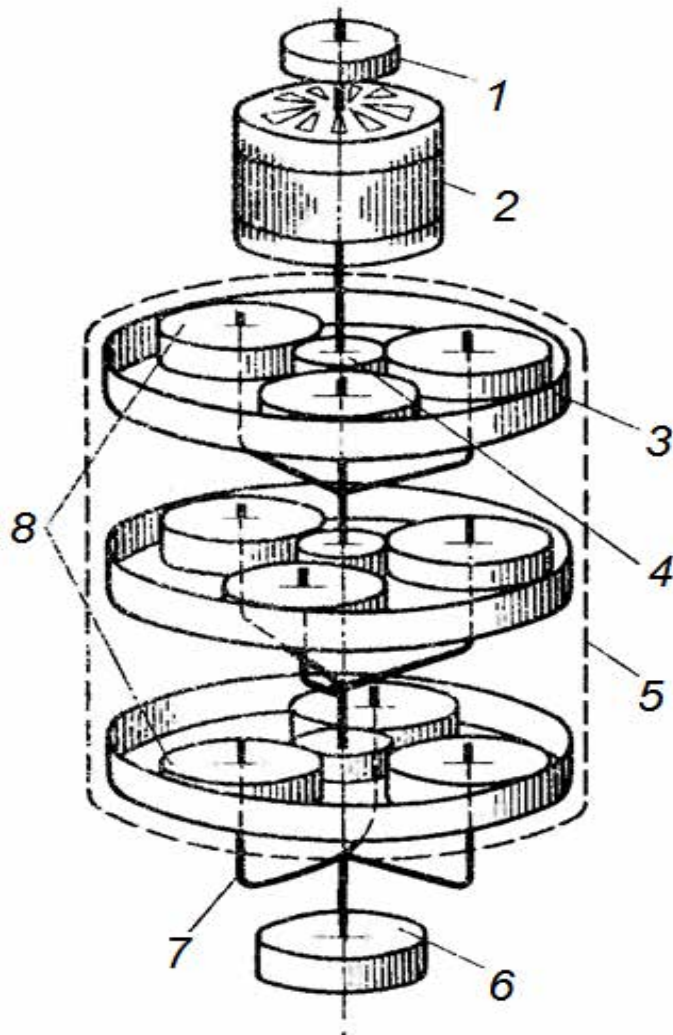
Механізм повороту баштового крана з планетарним редуктором
